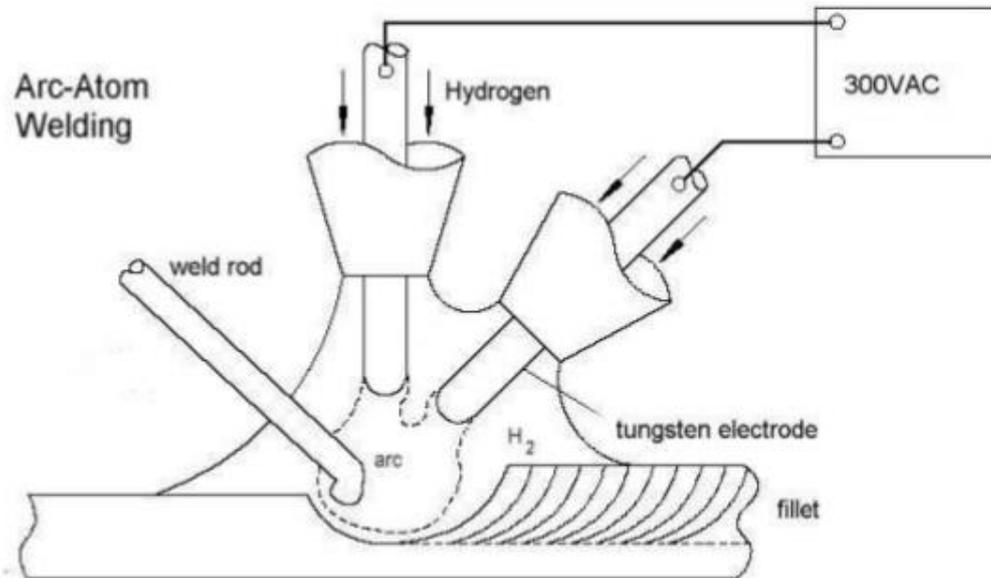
Soldadura con hidrógeno atómico (Fuente: slideshare.net)
